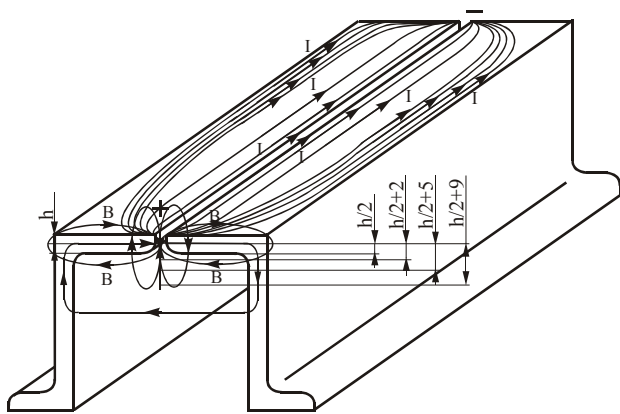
Методика измерения магнитного поля сварочного тока в зетовых профилях: I – сварочный ток; B – силовые линии магнитного поля
